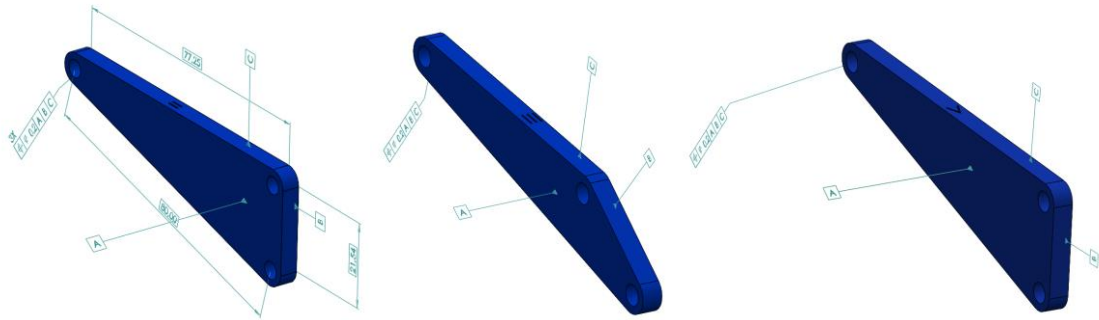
Tolerancias geométricas “Barra 1” dedos
